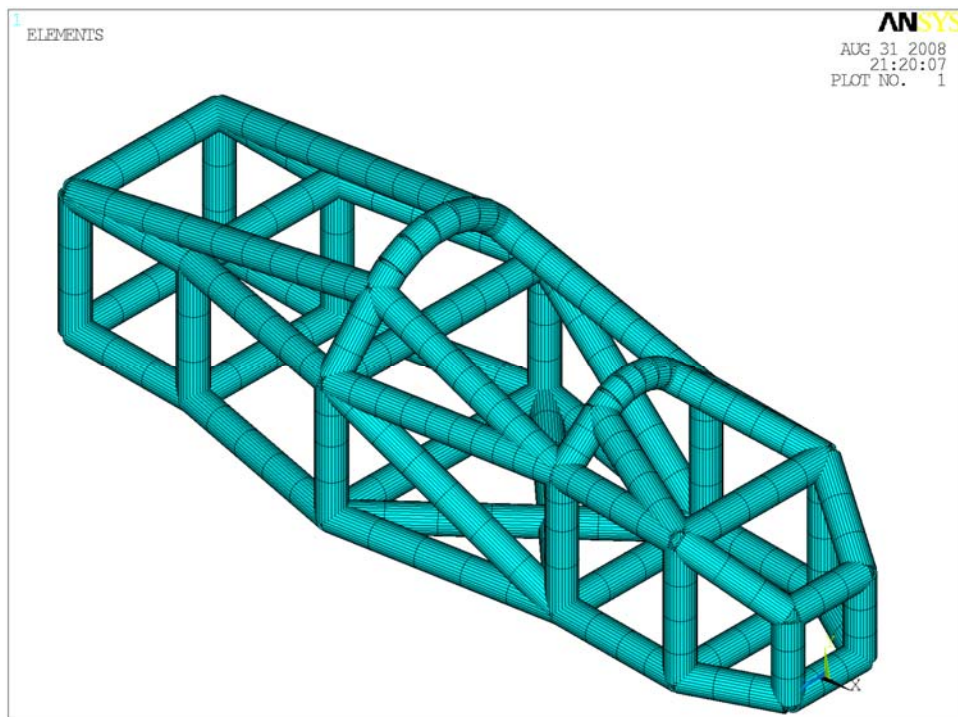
Enmallado de la Estructura, Elemento BEAM188
